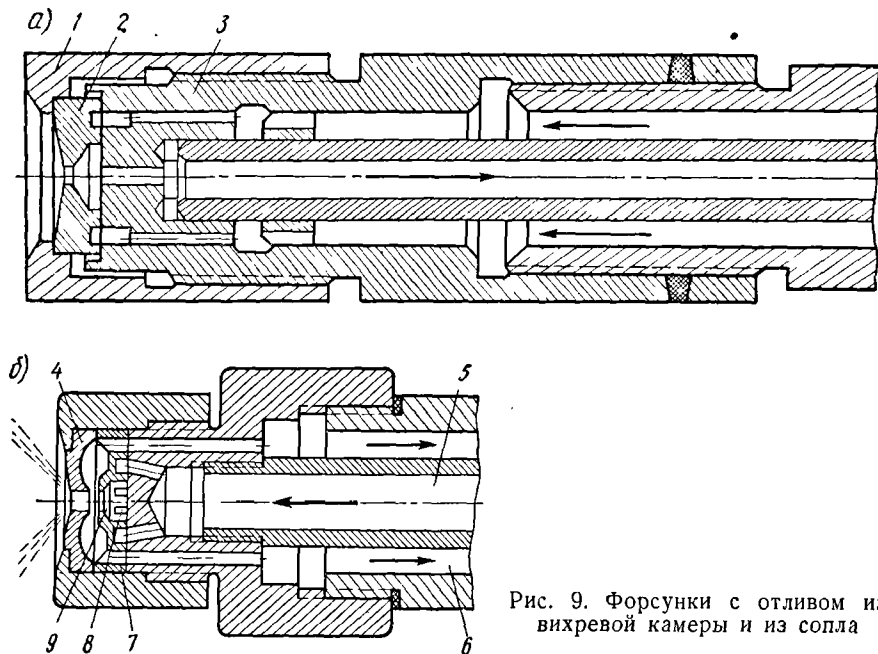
Форсунки с отливом из вихревой камеры и из сопла
